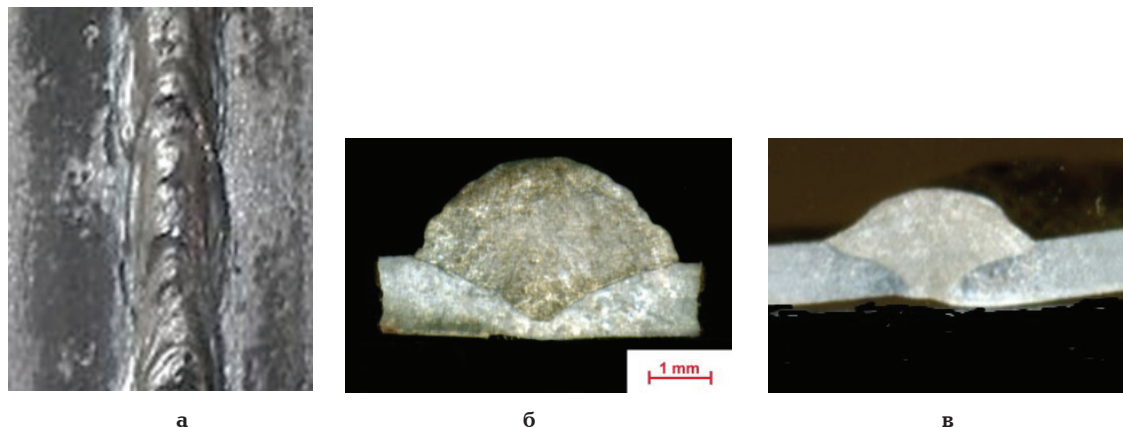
Особенности формирования швов: внешний вид сварного шва — а; сечение наплавленного металла — б; сечение сварного стыка, сваренного «на весу» при толщине листа 1 мм — в
